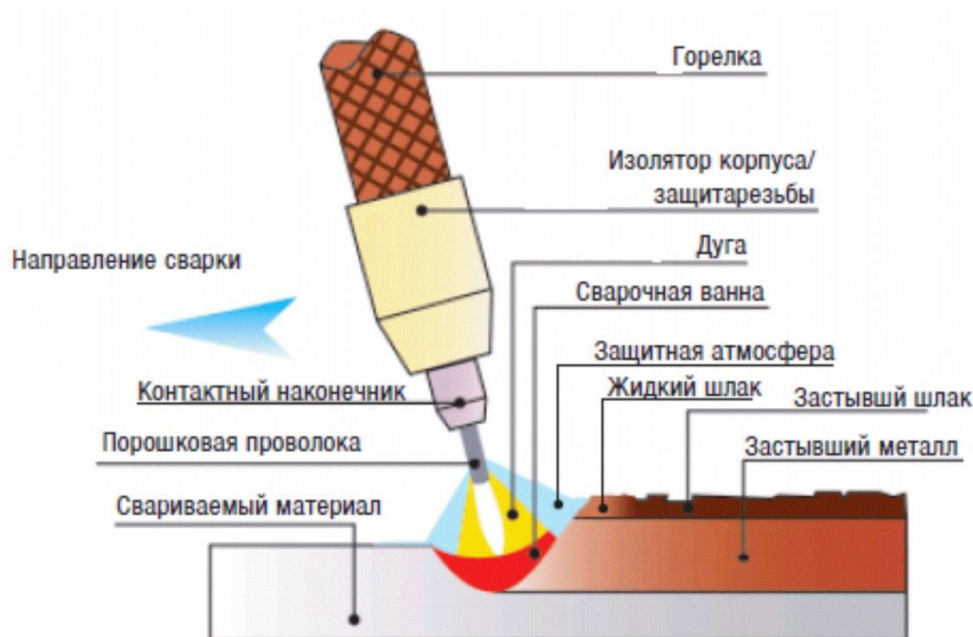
Схема сварки порошковой самозащитной проволокой
